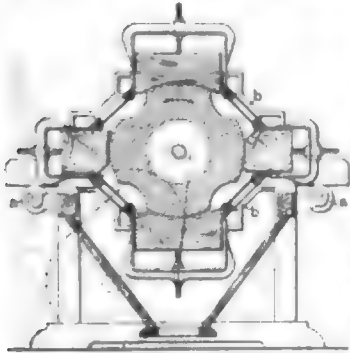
Mantelantrieb für Schäl- und Bürstmaschinen.
